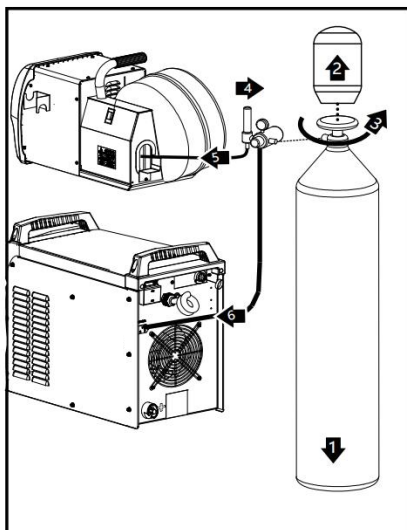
Conjunto de componentes del cable de soldadura
